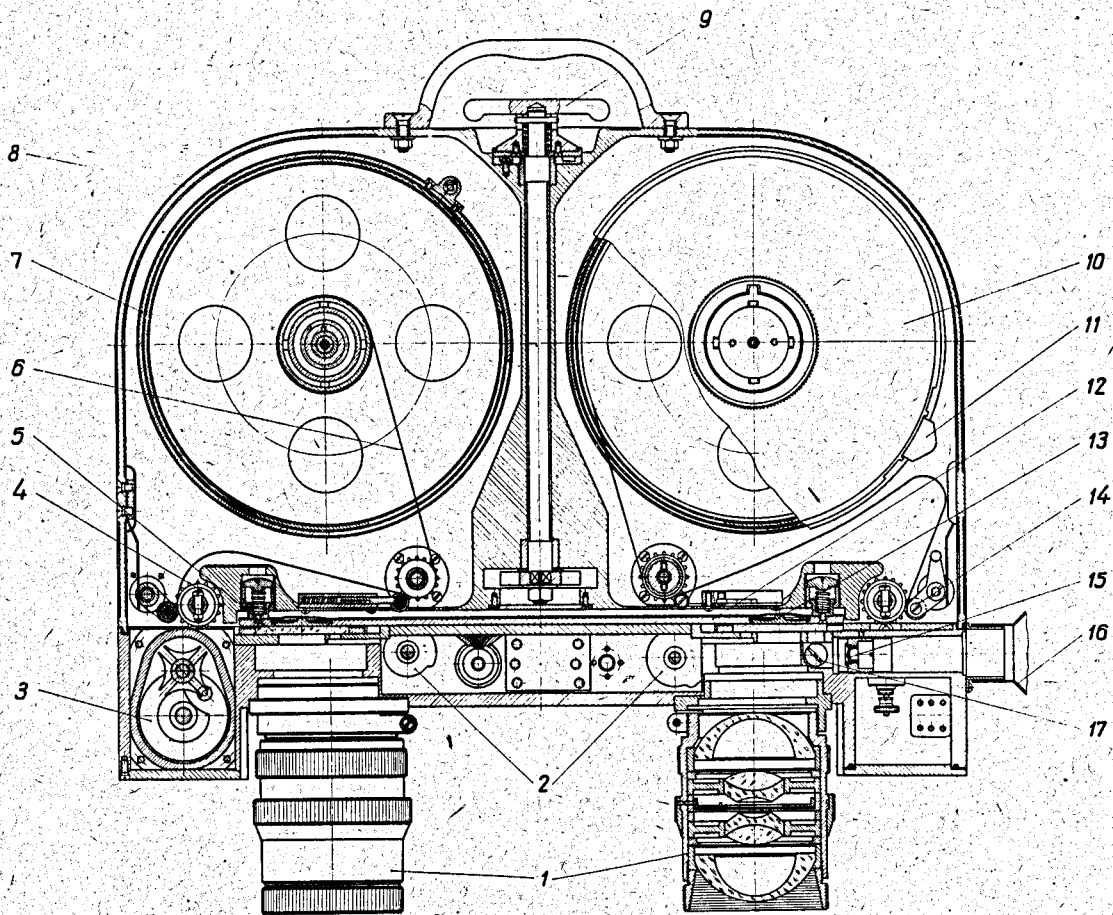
Схематический чертеж стереофотоаппарата. 1 - объективы; 2 - кулачки подъема прижимного столика; 3 - мальтийский механизм; 4 - лентопротяжный ролик; 5 - компенсационное выравнивающее стекло; 6 - пленка; 7 - приемная катушка; 8 - кассетница; 9 - рукоятка фиксатора; 10 - кассета с подающей бобиной пленки; 11 - замок кассеты; 12 - прижимной столик; 13 - индивидуальные дисковые прижимы пленки; 14 - направляющий ролик; 15 - однолинзовый объектив; 16 - часть тубуса приставки (не показанной на рисунке) для фотографирования на пленку условий опыта; 17 - зеркало.
